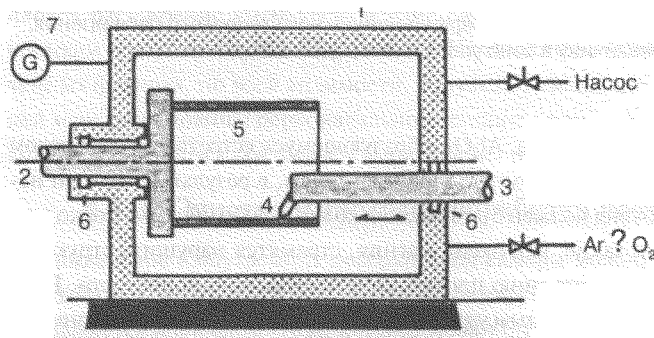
Схема процесса механической обработки EX: 1 — вакуумная камера; 2 — ось токарного станка; 3 — ось инструмента; 4 — инструмент; 5 — обрабатываемая деталь; 6 — вакуумное уплотнение; 7 — вакуумметр (источник: Н. Ishimaru, "Development and Application for All-Aluminum Alloys Vacuum System" *MRS Bulletin*, Vol. XV, No 7, 1990)
